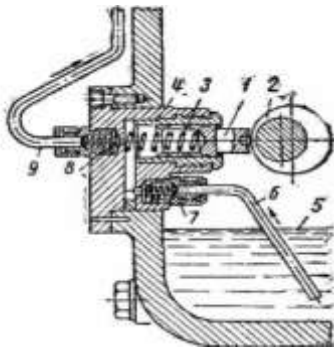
Плунжерный насос для циркуляционной смазки: 1 — плунжер; 2 — эксцентрик, насаженный на вал механизма; 3 — пружина, прижимающая плунжер к эксцентрику; 4 — цилиндр плунжера; 5 — маслобункер; 6 — всасывающий маслопровод; 7 и 8 — обратный шариковый клапан; 9 — нагнетательный маслопровод.
